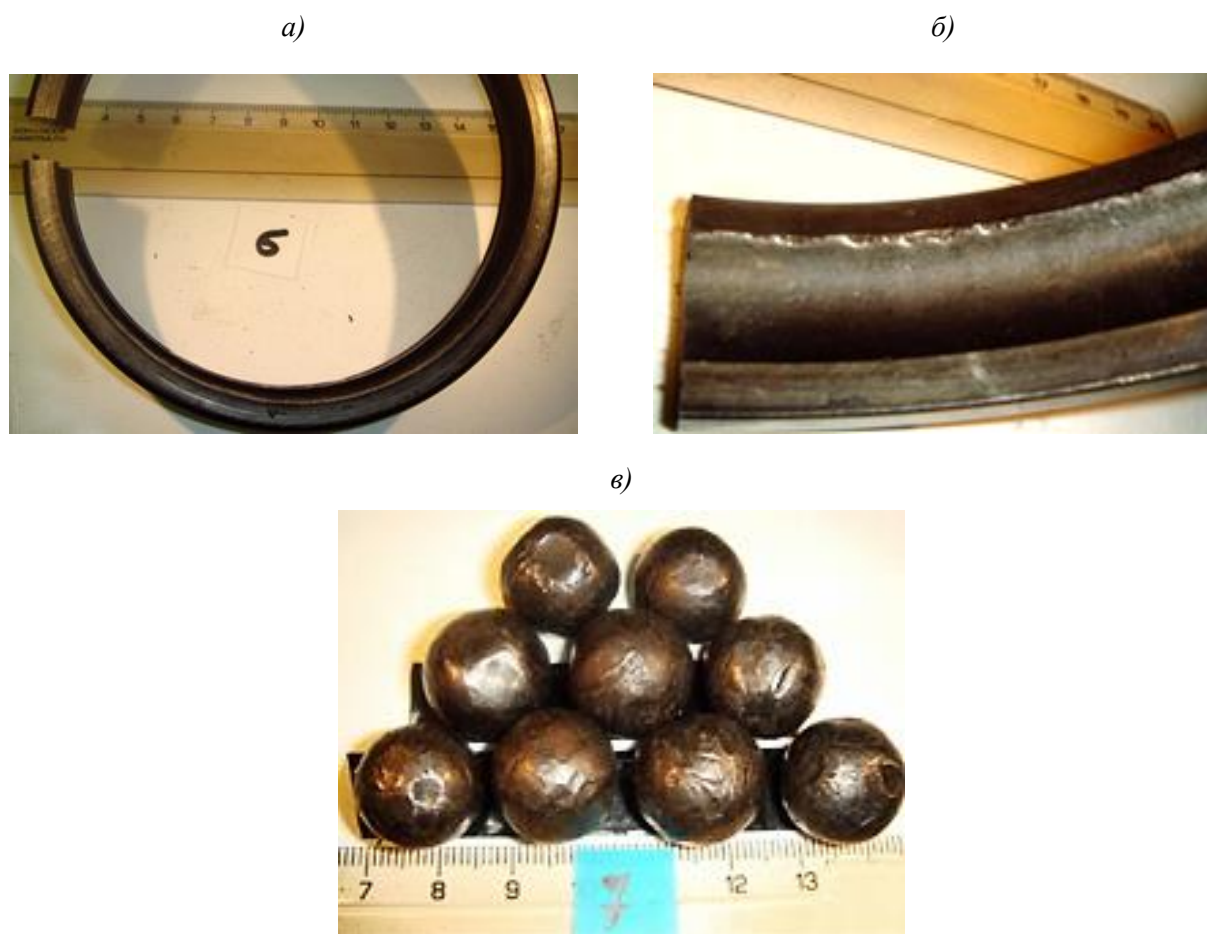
Внешний вид разрушенного шарикоподшипника из стали ШХ15:
